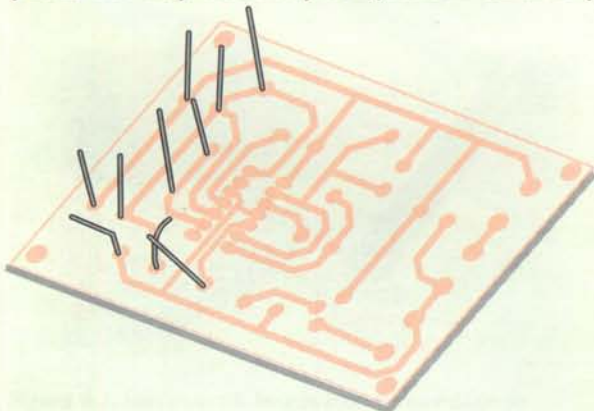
Montaje de algunos componentes para su soldadura
